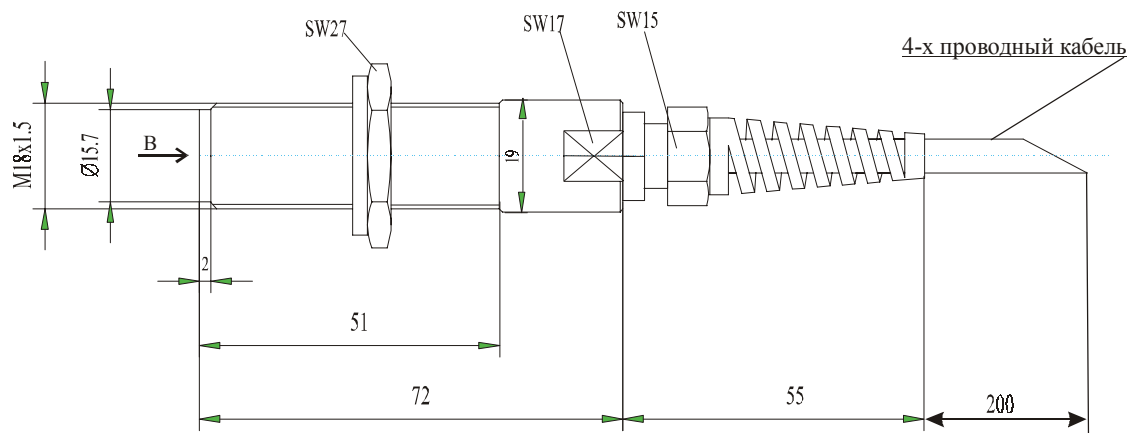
Внешний вид и габаритные размеры датчиков типа SMP4.GR07.T1
